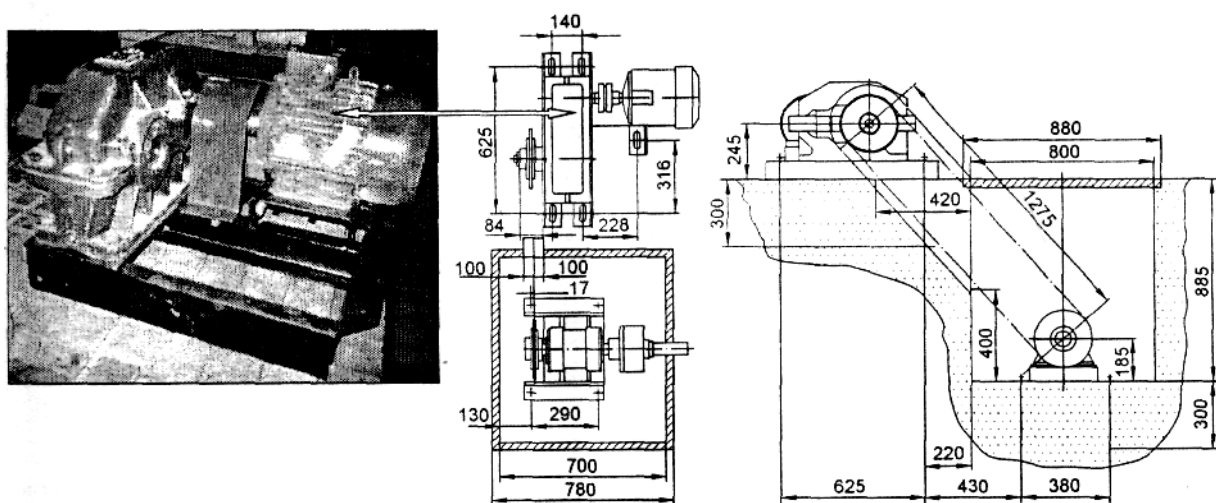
Схема монтажа приводной станции шнекового навозоуборочного транспортера
